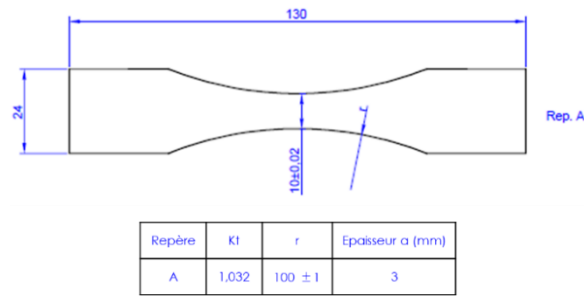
Schéma et dimensions des éprouvettes TdG (Taille de Guêpe) utilisées pour les essais de durée de vie
